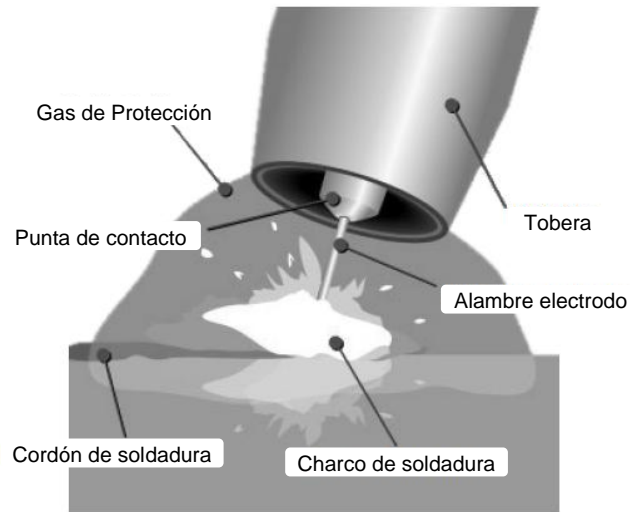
Esquema del proceso de soldadura GMAW (1).
